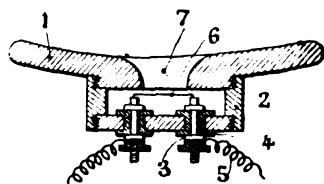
Premier type de récepteur thermique de MM. Abraham et Carpentier.
